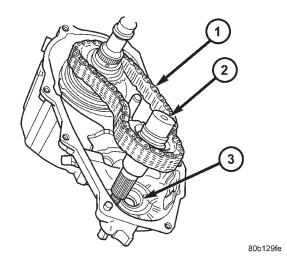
Desmontaje del eje transmisor delantero y la cadena propulsora
